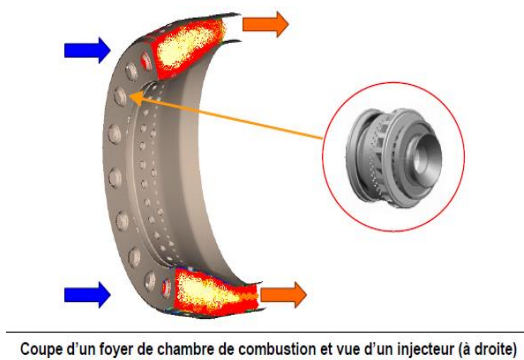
coupe d'un foyer de chambre de combustion et vue d'un injecteur
